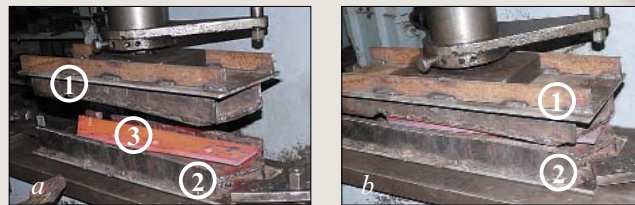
Штамповка лемеха: а – положение перед работой; б – момент прижатия пуансона к матрице с заготовкой лемеха: 1 – пуансон; 2 – матрица; 3 – лемех
